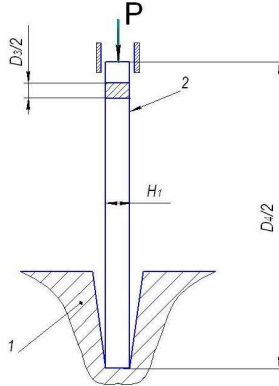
Расчетная схема устойчивости диска: 1 – заготовка; 2 – инструмент-диск
